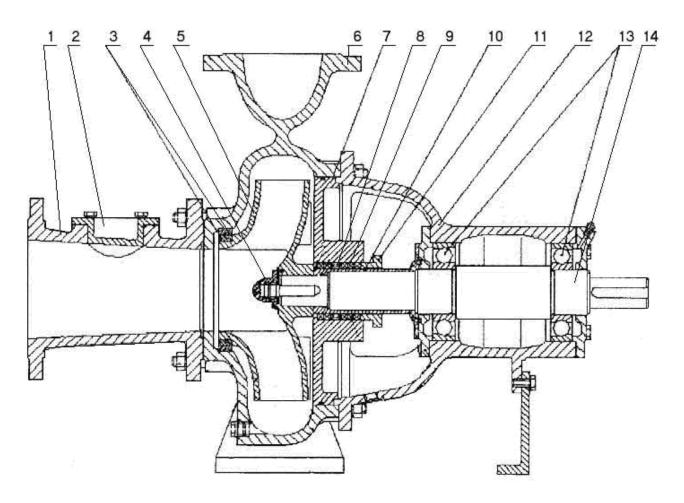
Разрез насоса СМ: 1 — всасывающий патрубок; 2 — люк для прочистки полости насоса; 3 — уплотняющие кольца рабочего колеса; 4 — гайка крепления рабочего колеса; 5 — рабочее колеса; 6 — корпус с напорным патрубком; 7 — корпус сальникового уплотнения вала; 8 — кольцо гидравлического уплотнения сальника; 9 — сальниковая набивка; 10 — защитная втулка вала; 11 — крышка сальника; 12 — кронштейн; 13 — подшипники; 14 — вал насоса
